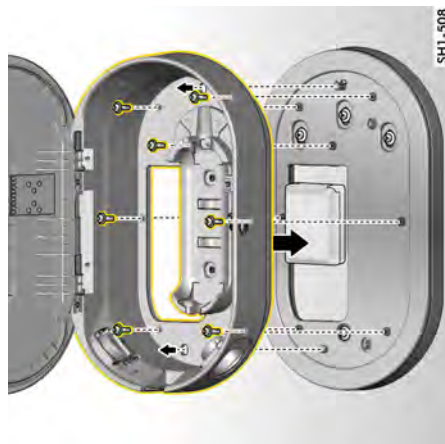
Cómo atornillar el puerto de carga a la placa de montaje
